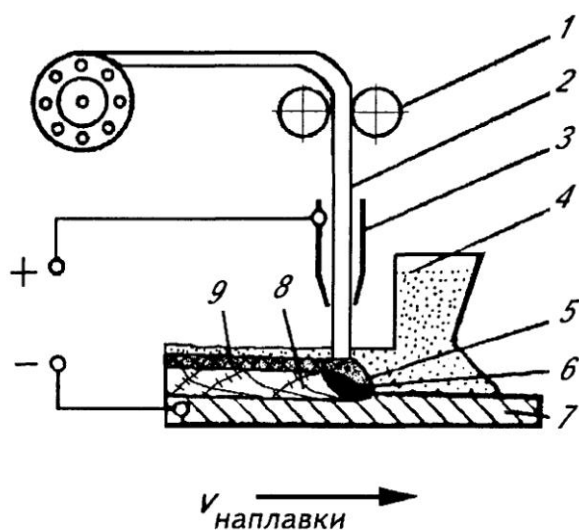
Схема электрошлаковой наплавки: 1 – подающий механизм; 2 – наплавочный материал; 3 – токоподвод-мундштук; 4 – гранулированный шлак; 5 – шлаковая ванна; 6 – сварочная ванна; 7 – обрабатываемая поверхность; 8 – наплавленный металл; 9 – корочка шлака
